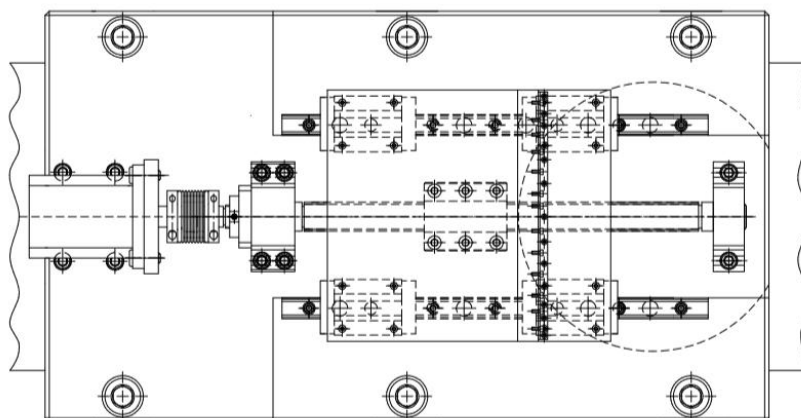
Вид сверху 3-х координатного фрезерно-мобильного станка
